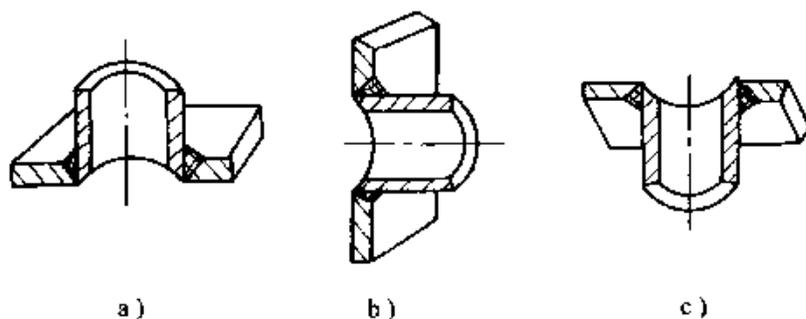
管板全焊透角焊缝试件 (TPG)
